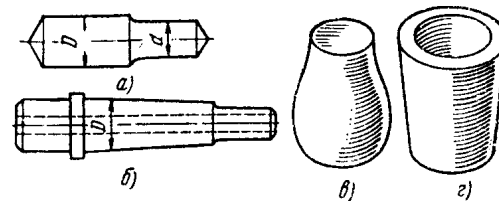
Оправки: а — для раскатки (дорн), б — пустотелая для протяжки, в и г — фасонные для калибровки отверстий и колец
